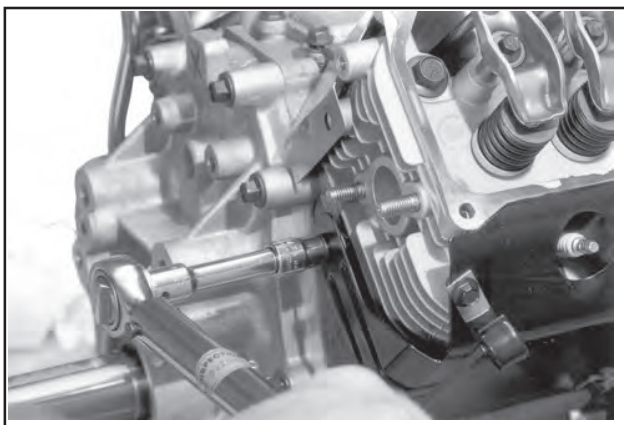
Die Befestigungsschrauben des Blechs anziehen.
